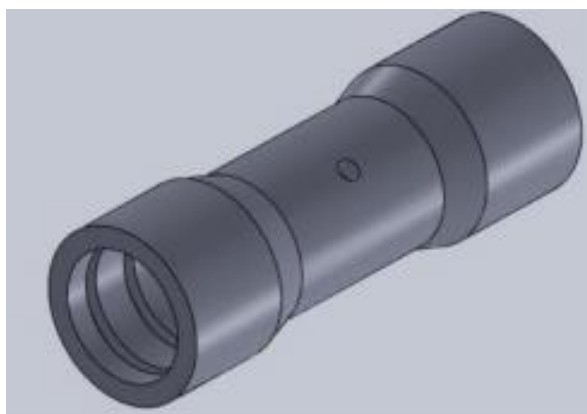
Desenho Técnico da conexão para tubulação de acrílico.
